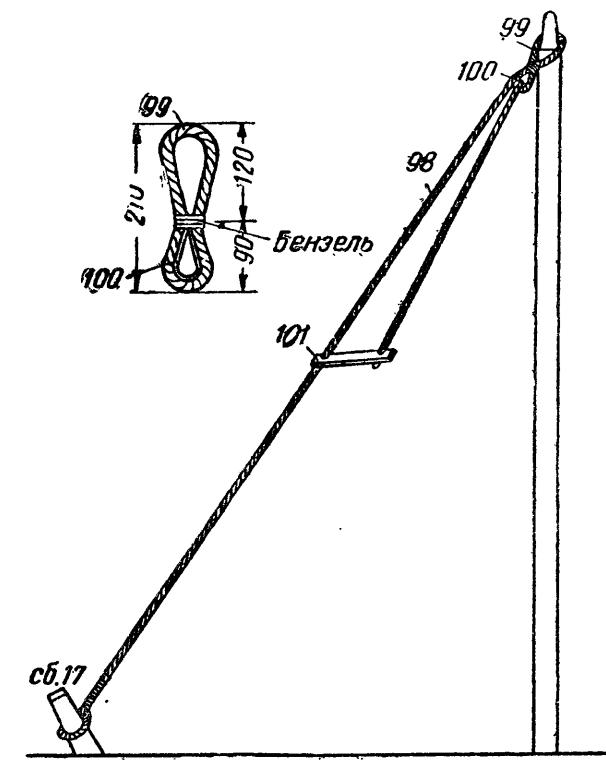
Оттяжка: 98 — веревка оттяжки боковых стоек; 99 — веревка стропки; 100 — коуш; 101 — ручка-натяжка
